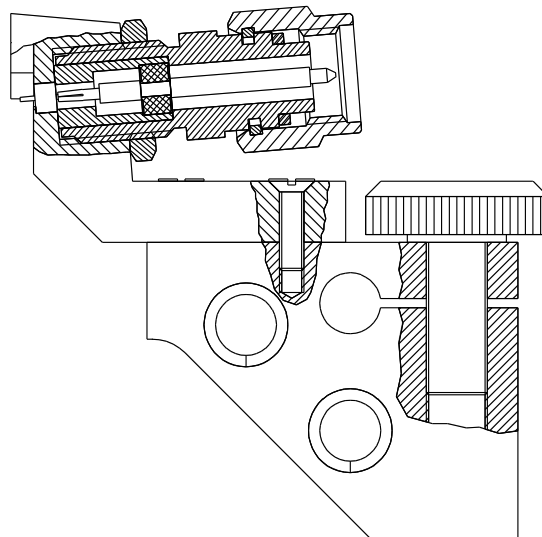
Schnittbild des Messkopfes mit 2.92mm-Stecker
